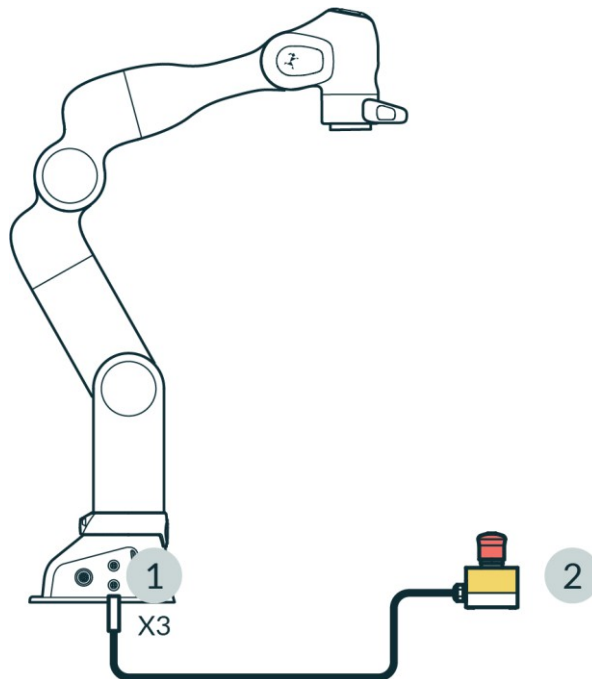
Collegamento del dispositivo di arresto di emergenza
